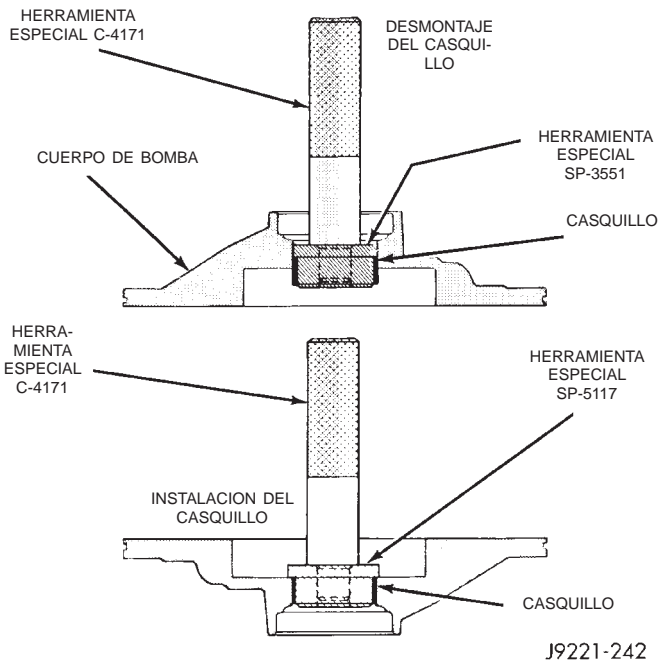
Desmontaje del casquillo de la bomba de aceite
